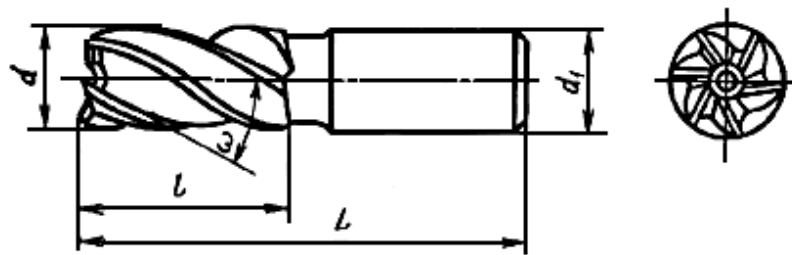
кінцева фреза з циліндричним хвостиком 2220-0021 ГОСТ 17025-71
